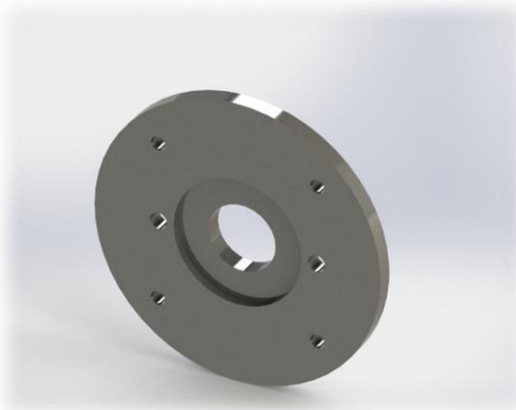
Flange dos motores de passo dos eixos X, Y e Z.
